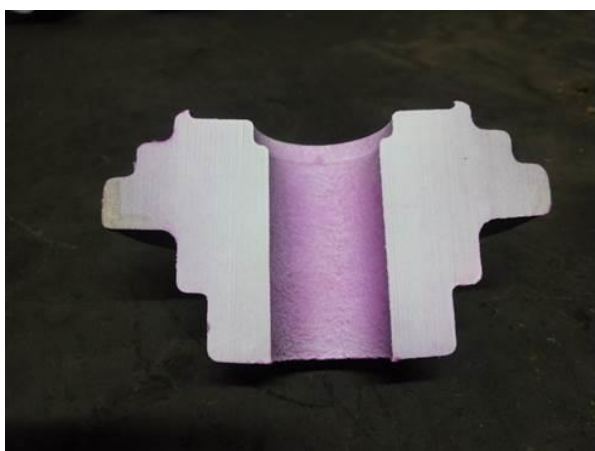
Foto da peça 9, cortada segundo o plano de separação, depois do ensaio de Líquidos Penetrantes.
